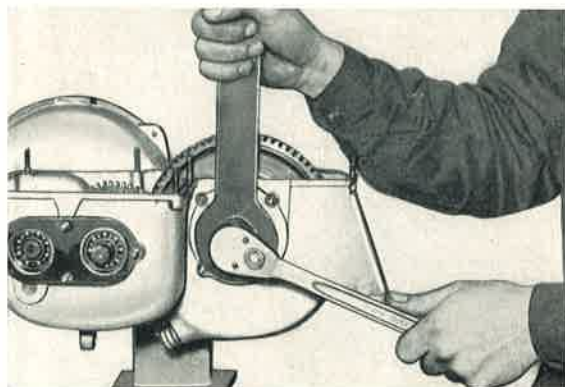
/2: Beim Abschrauben der Muttern für die Naben muß mit dem Halteschlüssel gegengehalten werden.
